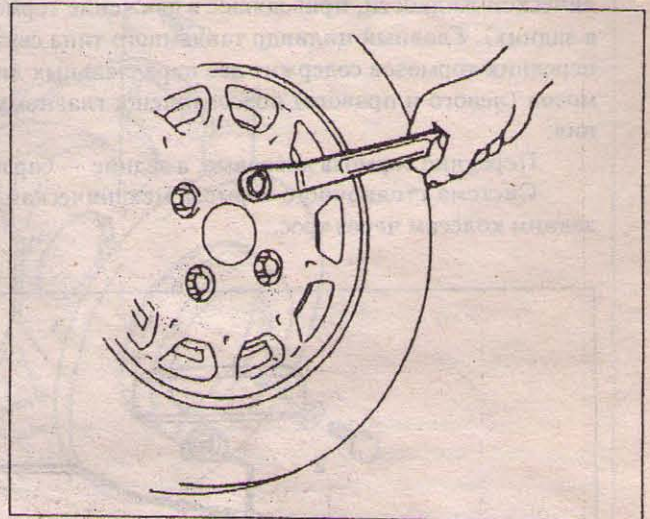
F—8 ЗАТЯЖКА ГАЙКИ КОЛЕСА
